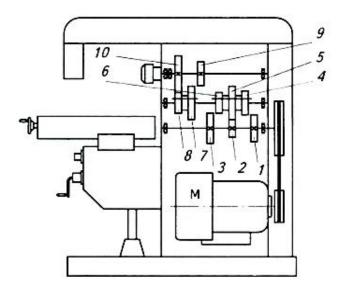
Упрощенная кинематическая схема фрезерного станка НГФ-110Ш: M — электродвигатель; 1—10 — зубчатые колеса и шестерни
